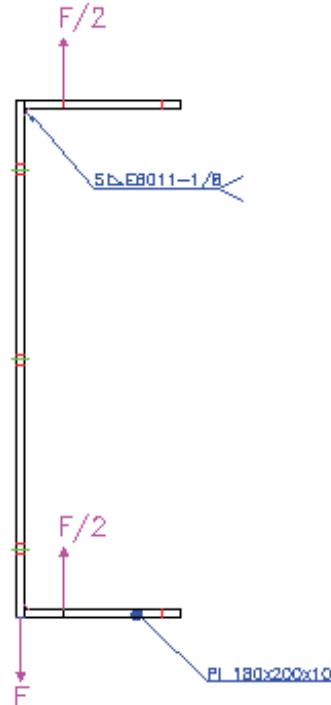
Diagrama de cuerpo libre de la soldadura.
